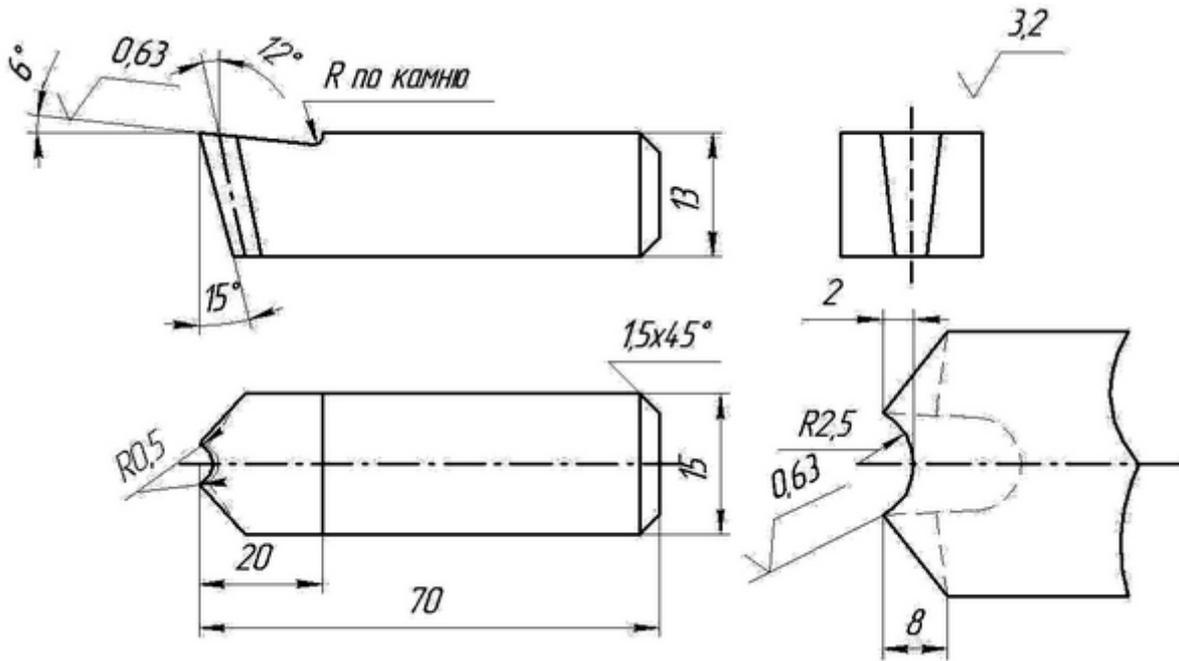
Конструкция резца для закругления торцов зубьев
